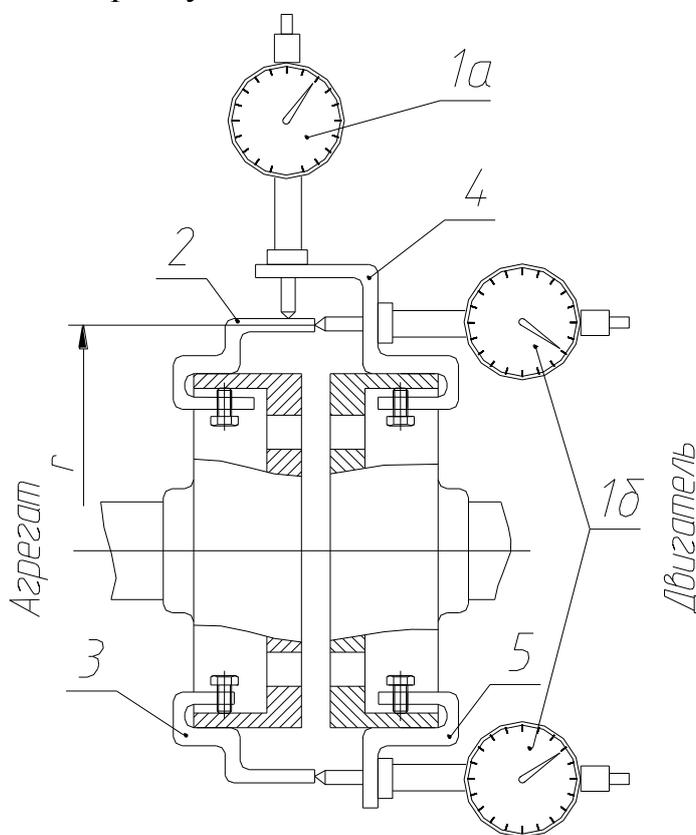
Приспособление для центровки, укрепленное на ободах полумуфт.
